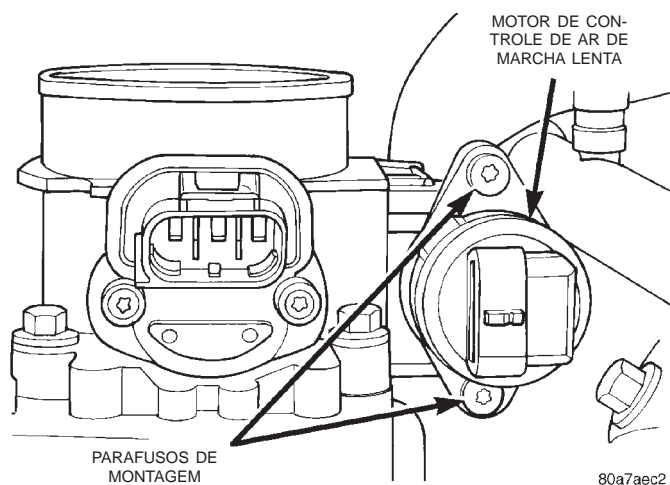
Cavilhas de Montagem (Parafusos)—Motor de IAC
